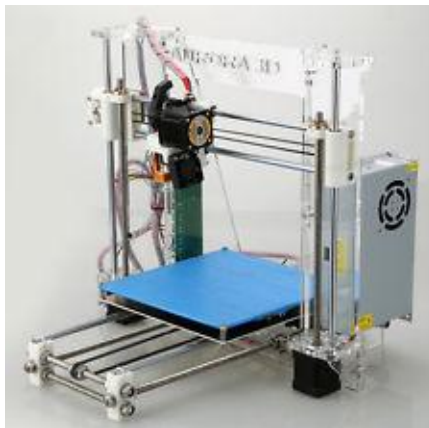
Загальний вид 3D-принтера Prusa i3 DIY
